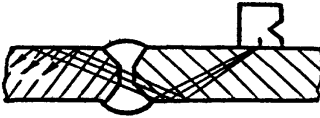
Схема перемещения искателя по поверхности при контроле сварного шва
